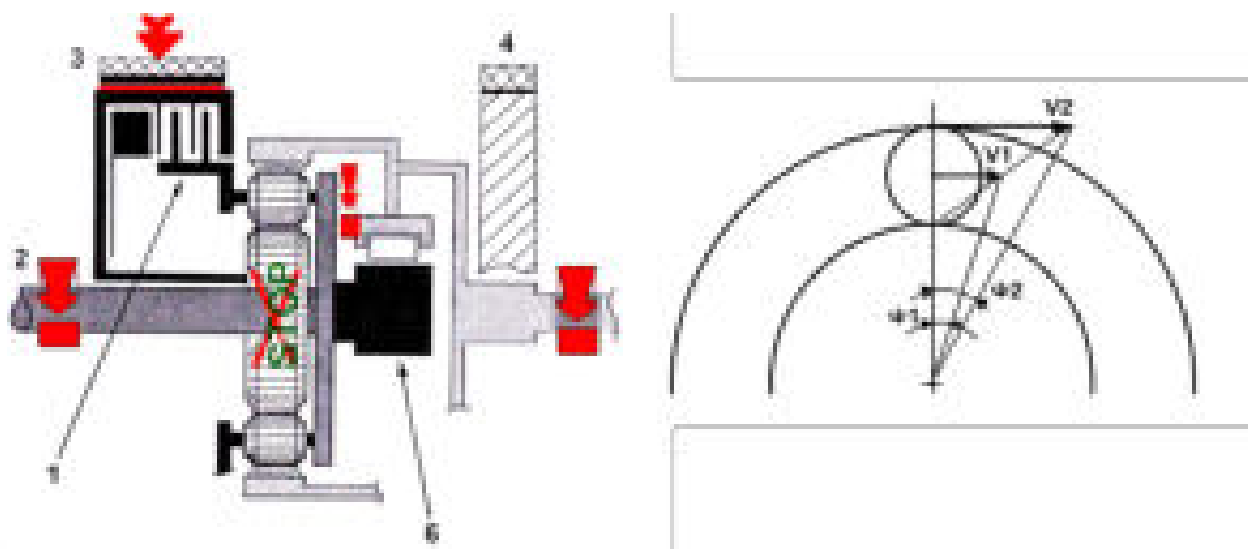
Повышающая передача дополнительного планетарного ряда.
